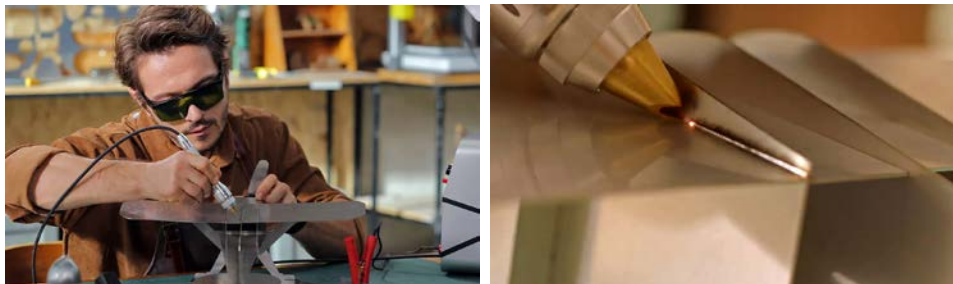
Лазерный сварочный аппарат X1 Pro
